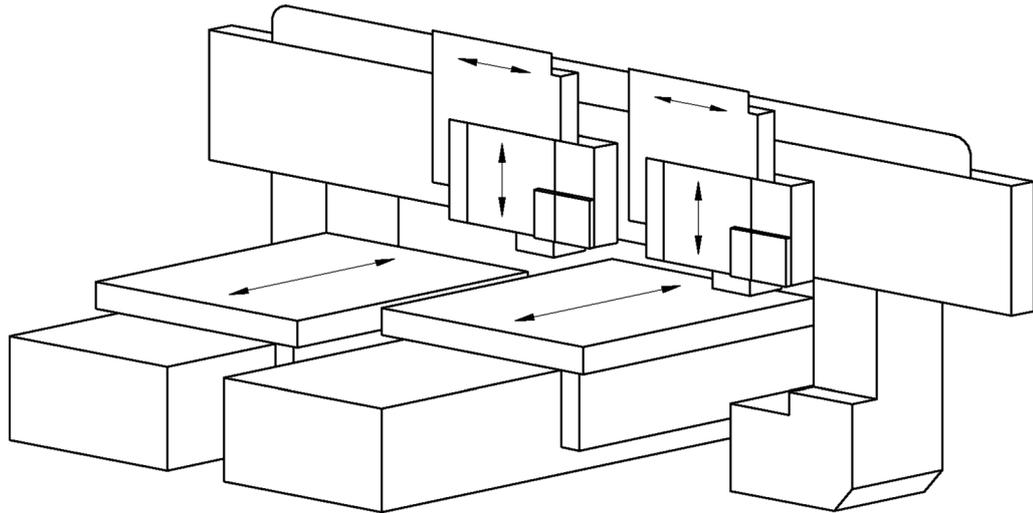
Exemple de machine à portique avec tables mobiles, portique fixe, têtes d'usinage mobiles
